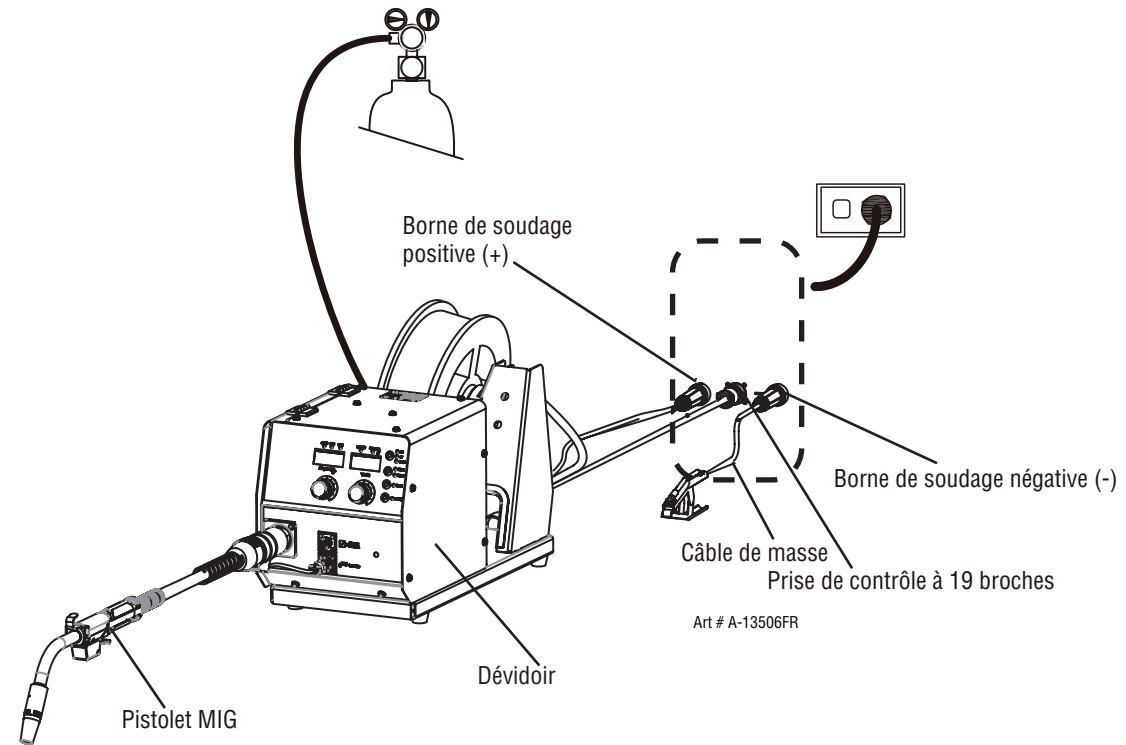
Configuration pour soudage MIG (GMAW) avec fil MIG sous protection gazeuse
